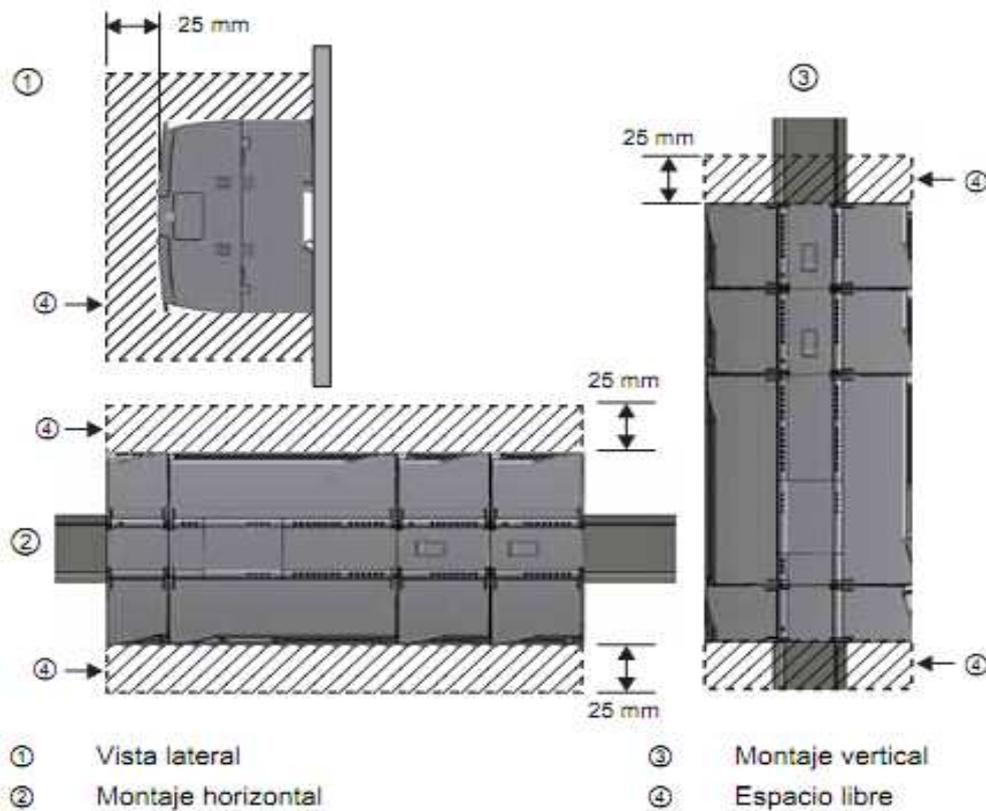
Dimensiones de montaje y espacio libre necesario. Parte A
